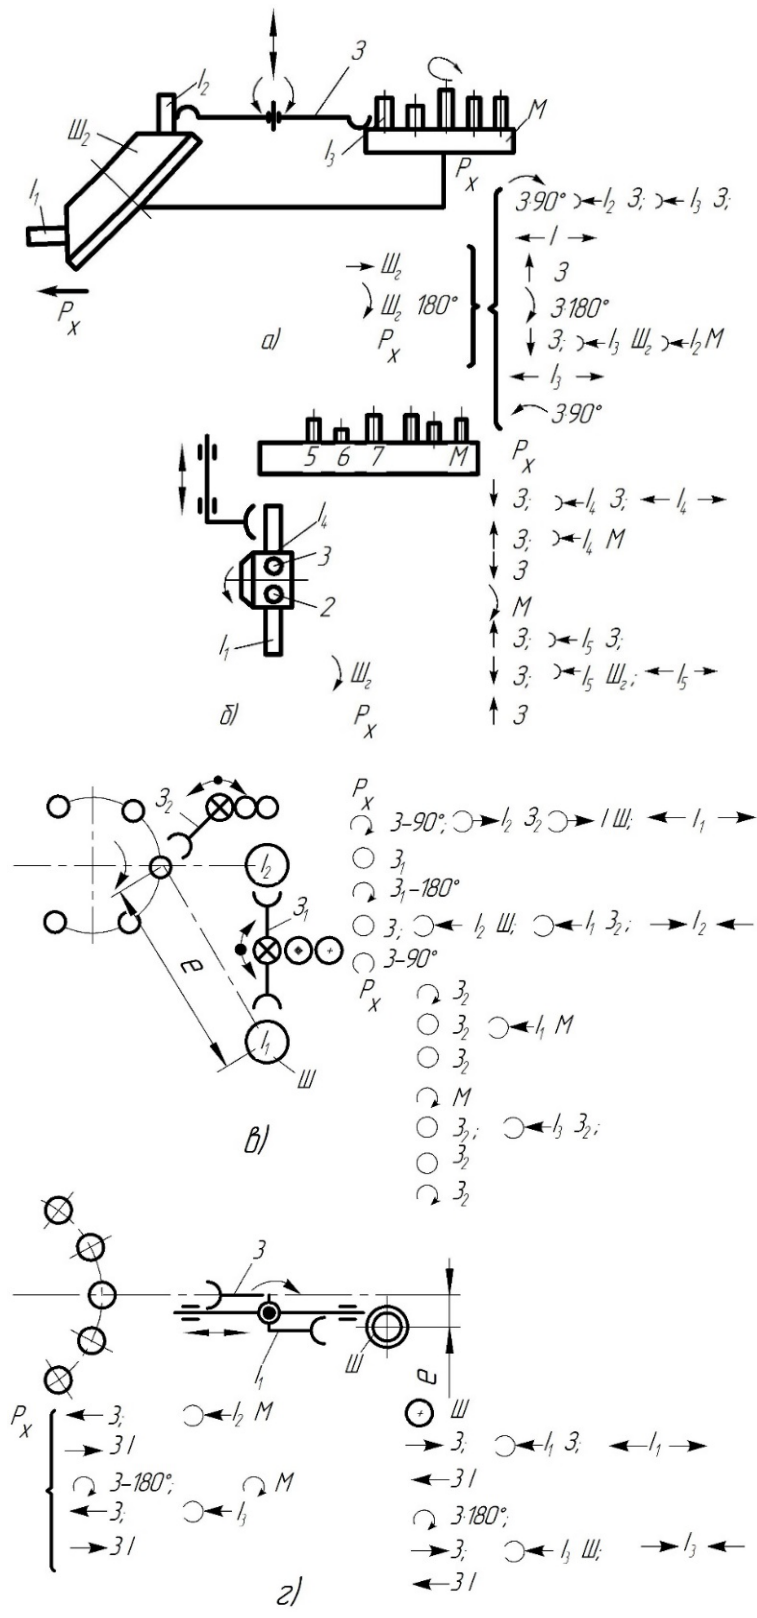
Двошпindelна револьверна головка з магазином, який знаходиться на шпindelній бабці
